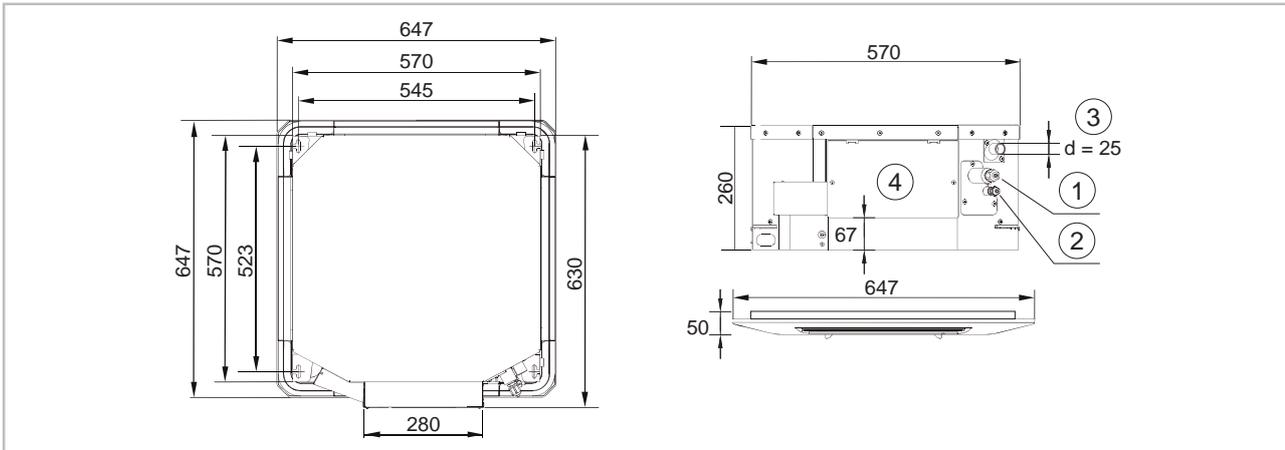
Abmessungen MVD 222-452 (Alle Angaben in mm)
